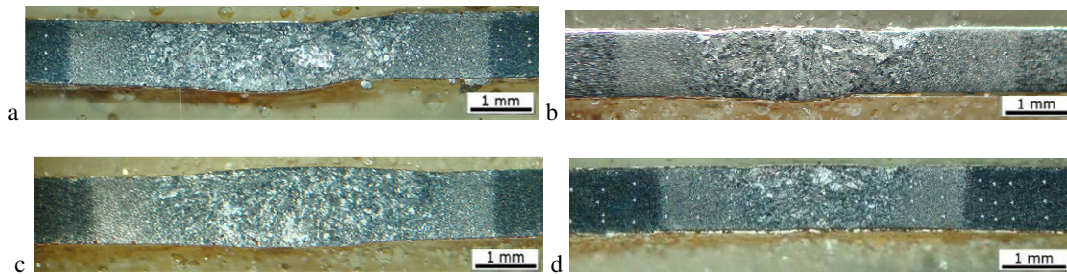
Probetas soldadas: a- 7 y b-11.
